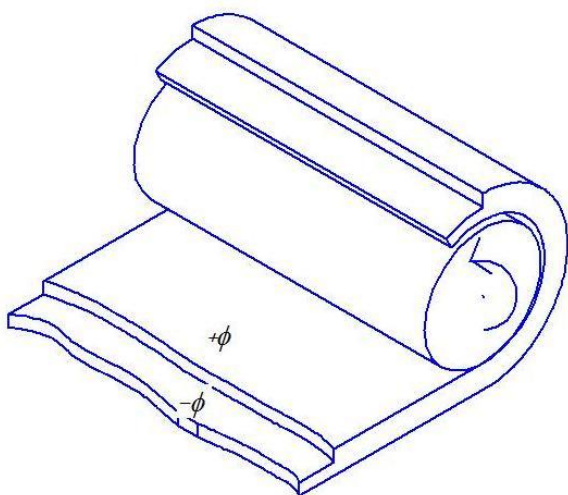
Сема изготовления трубчатых образцов из слоев препрега
